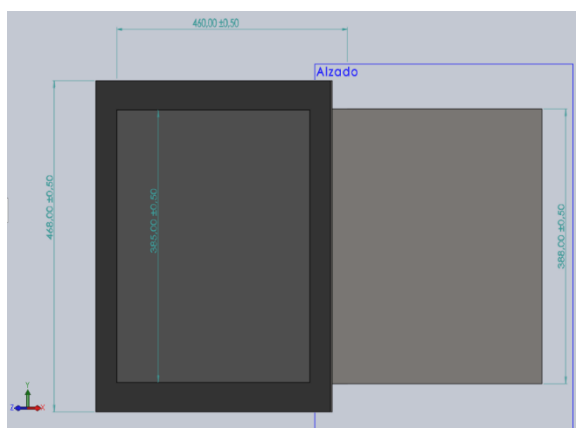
Perspectiva del modelo tridimensional de la sección de aspiración, con cotas expresadas en mm. Fuente propia.
